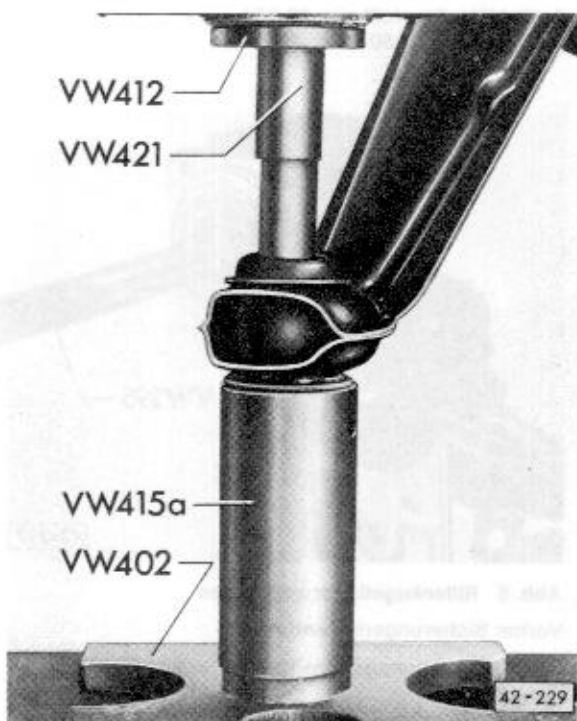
Innere Buchsen der Gummimetallager auspressen
